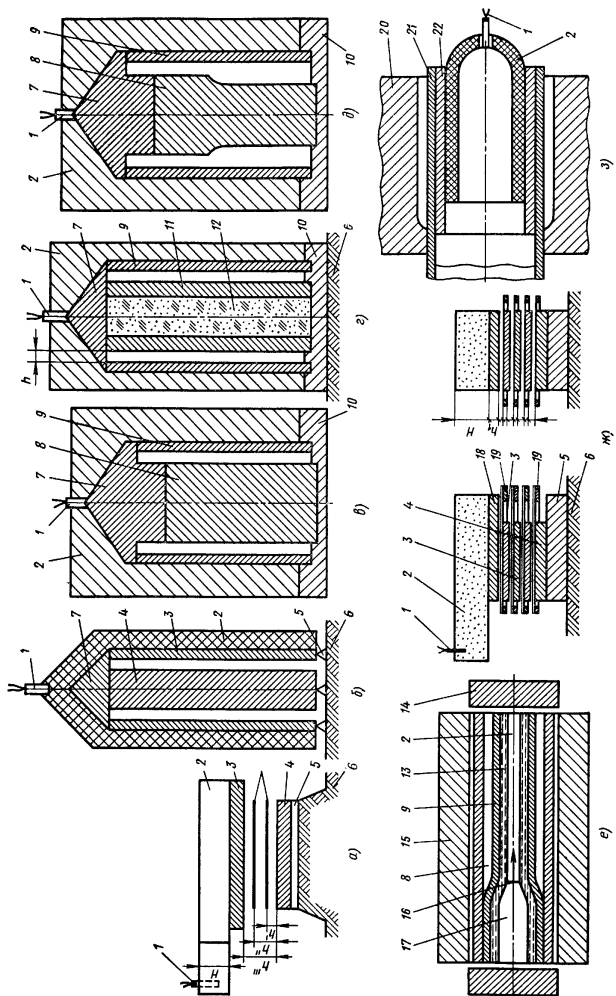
Технологические схемы сварки взрывом соединений различного типа:
